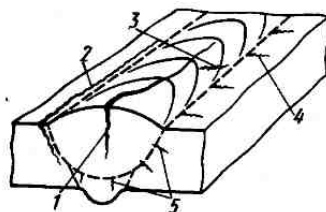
Горячие трещины в сварных соединениях:
